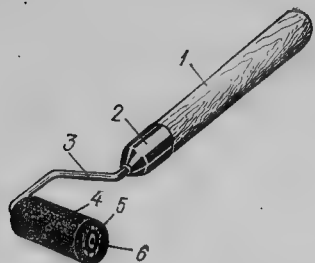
1 — ручка; 2 — колпачок; 3 — кронштейн; 4 — валик; 5 — корпус; 6 — ось
